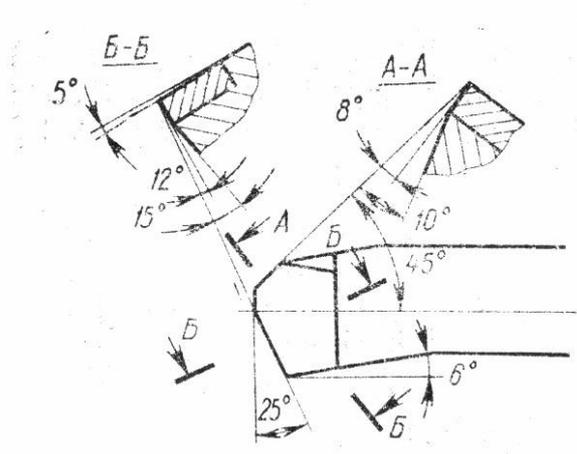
Токарный резец (правый проходной, подрезной, торцовый, расточной и фасочный) для комбинированной обработки
